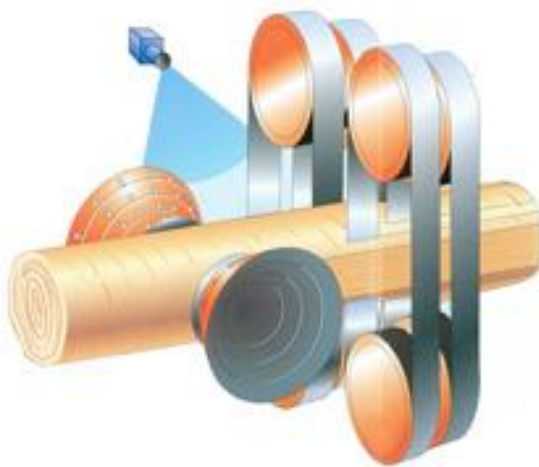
Схема использования ленточнопильного станка с фрезернобрусующим модулем
